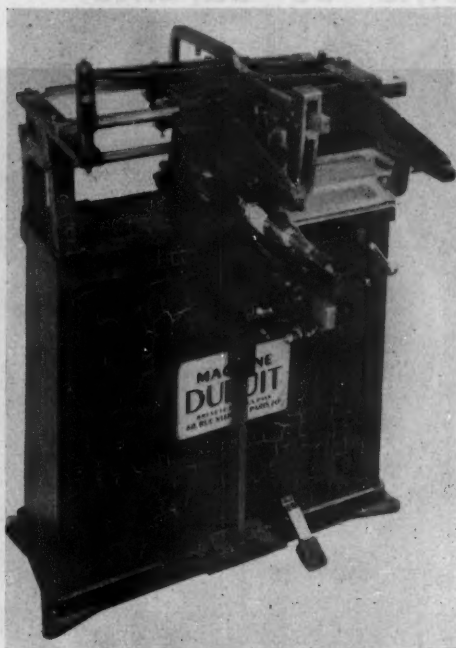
Machine Dubuit pour l'impression des bouteilles par sérigraphie.
